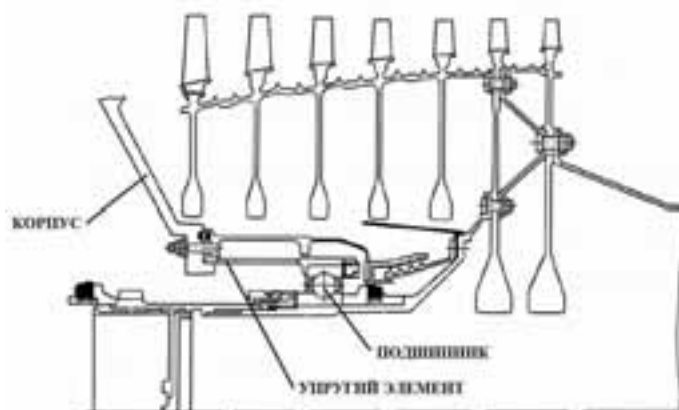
Схема опоры ротора компрессора высокого давления двигателя Д-36
